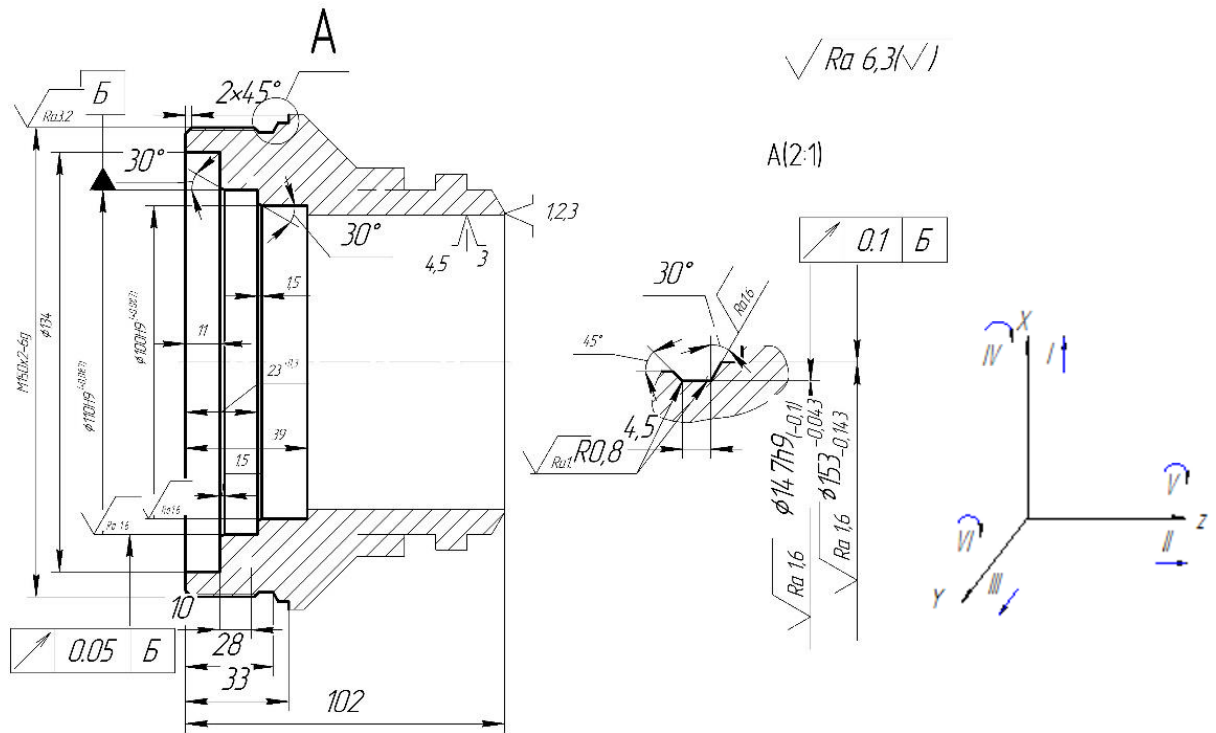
Схема базування заготовки на операції комплексній з ЧПК 015, позиція 3
